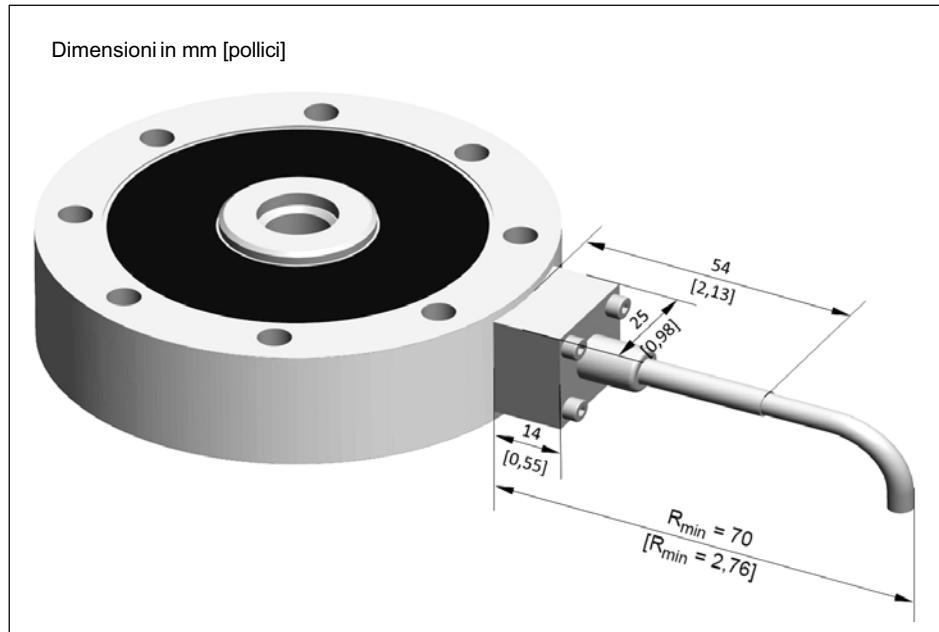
Ingombro d'installazione per cavo di collegamento fisso
